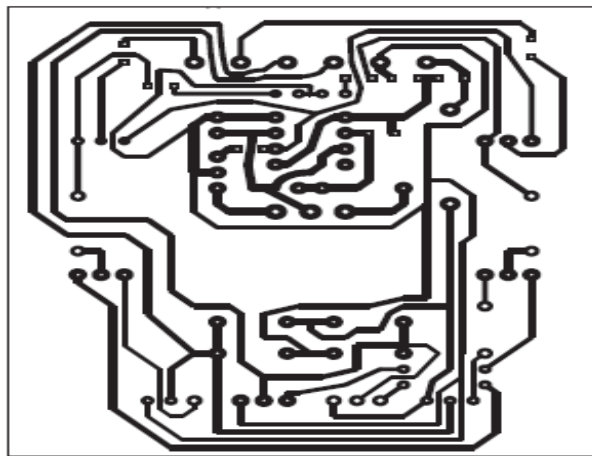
PCB tarjeta inversión de giro con control de velocidad
